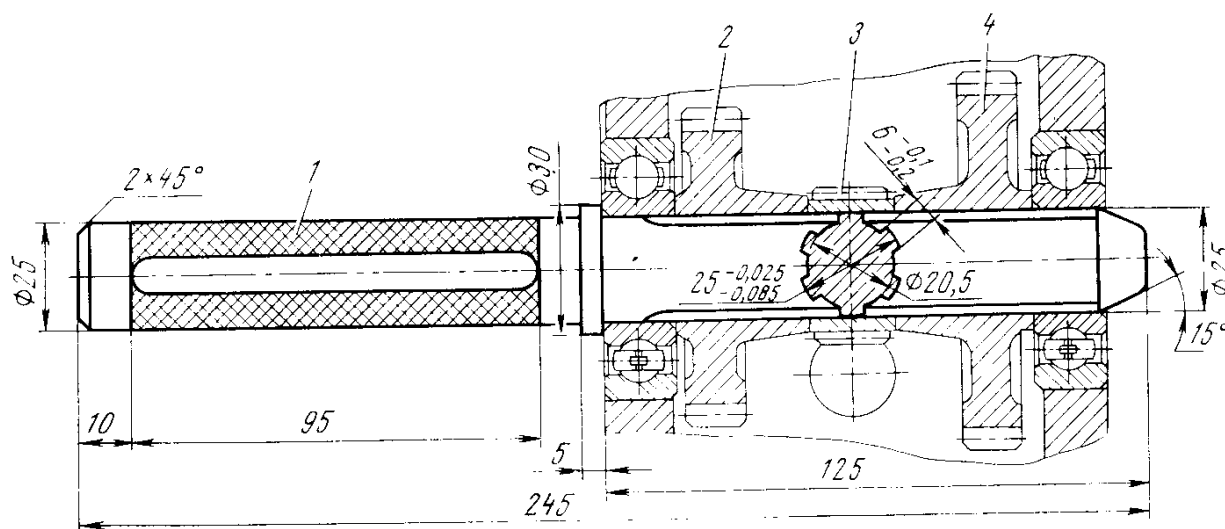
Оправка для удержания шестерен: 1 — оправка, 2 — ведомая шестерня IV передачи, 3 — ведущая шестерня привода спидометра; 4 — ведомая шестерня III передачи.
